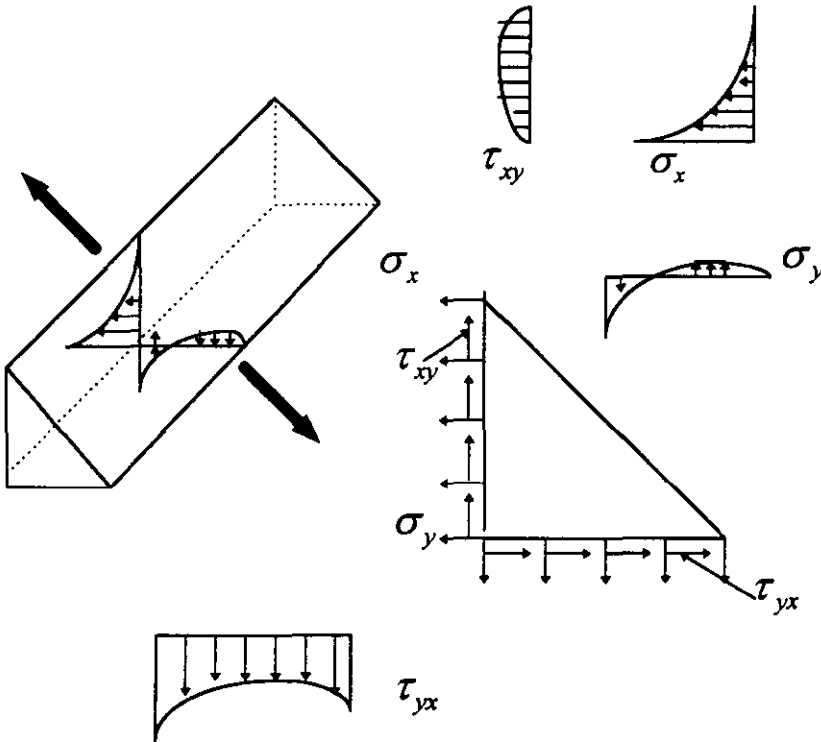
Esfuerzos en soldaduras de filete cargadas transversalmente
